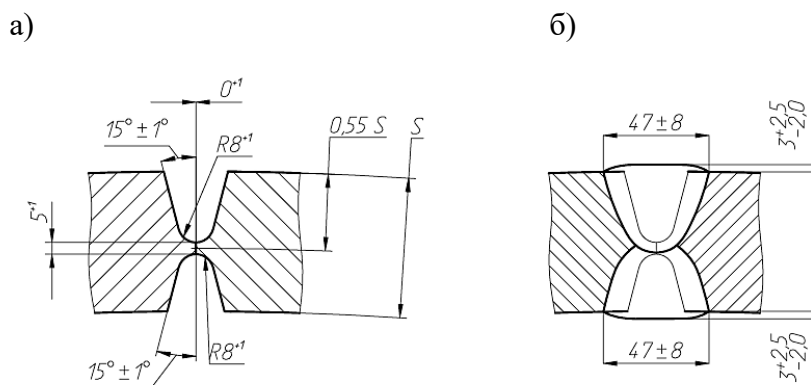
а) разделка кромок под сварку с углом $15^{\circ} \pm 1$, б) выполненное сварное соединение
